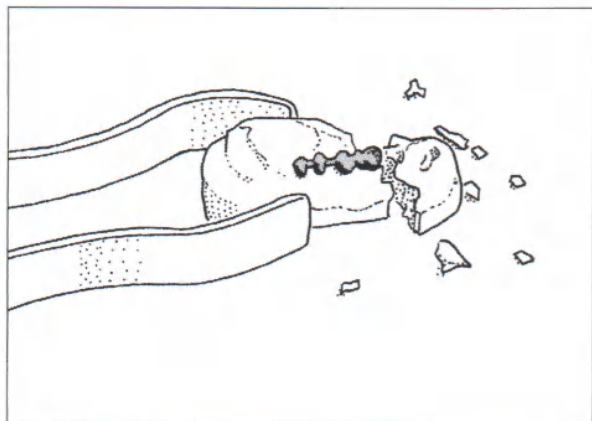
Формовочную массу удерживают литейными щипцами и разбивают ударом по прочной поверхности
